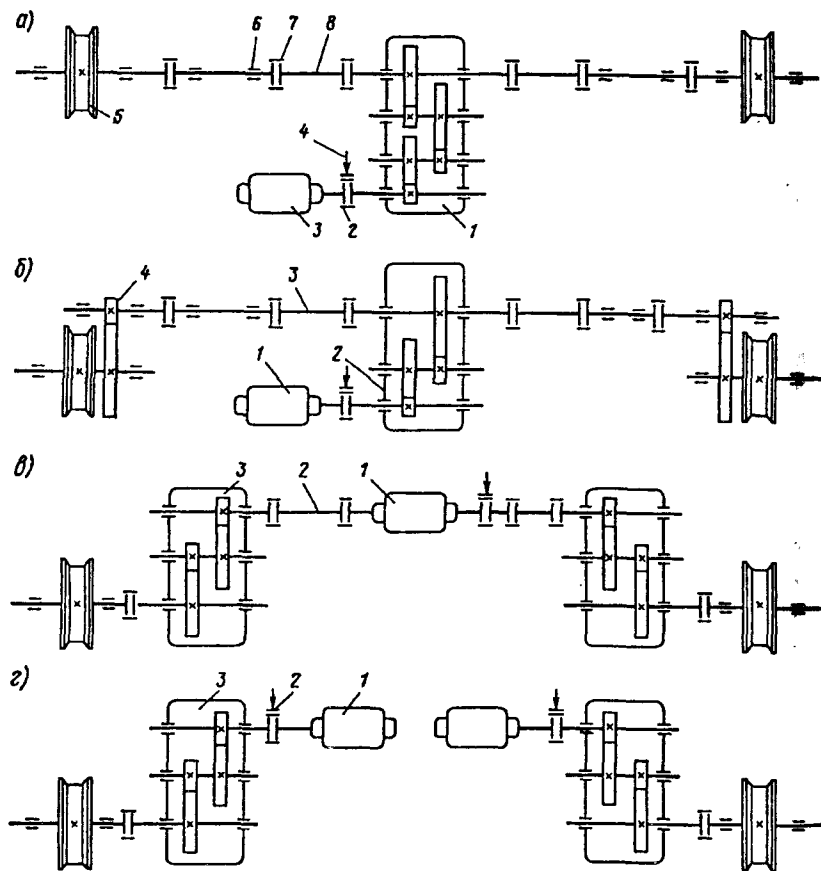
Схемы механизмов передвижения мостовых кранов: а — с тихоходным валом; б — со среднеходовым валом; в — с быстроходным валом; г — с отдельным приводом
